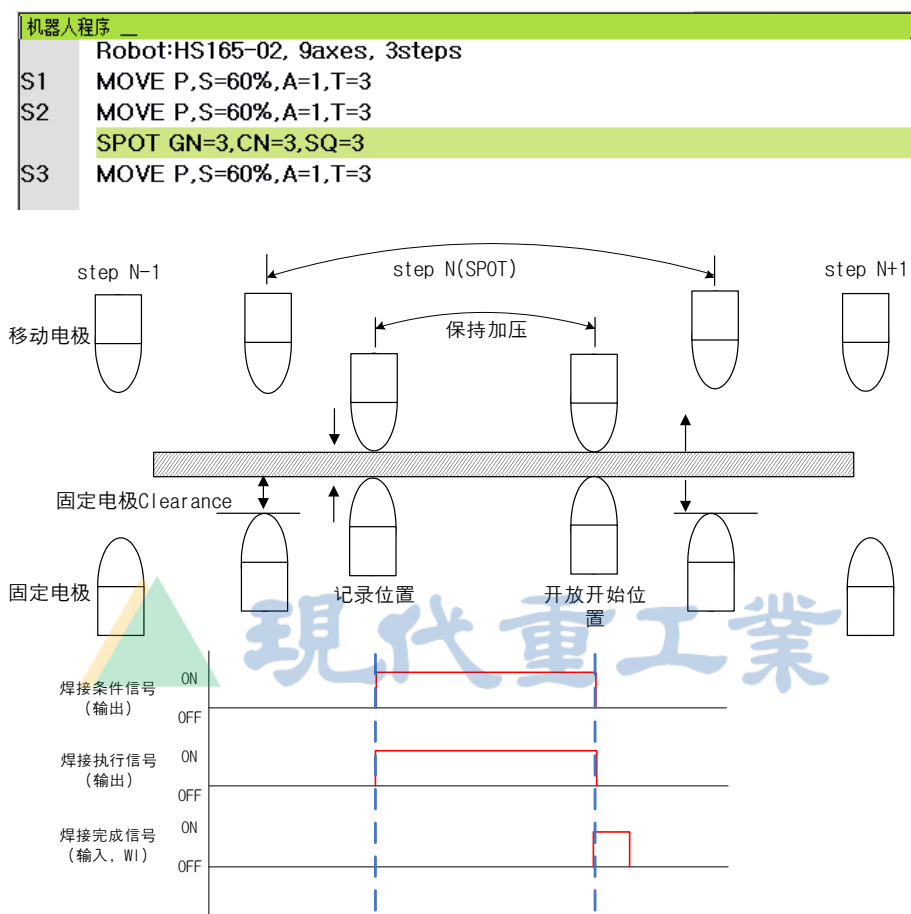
Eqlless 焊接枪点焊的再现
